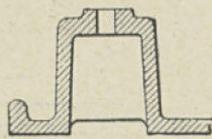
Bride étroite ne donnant pas un bon appui sur la fondation.
